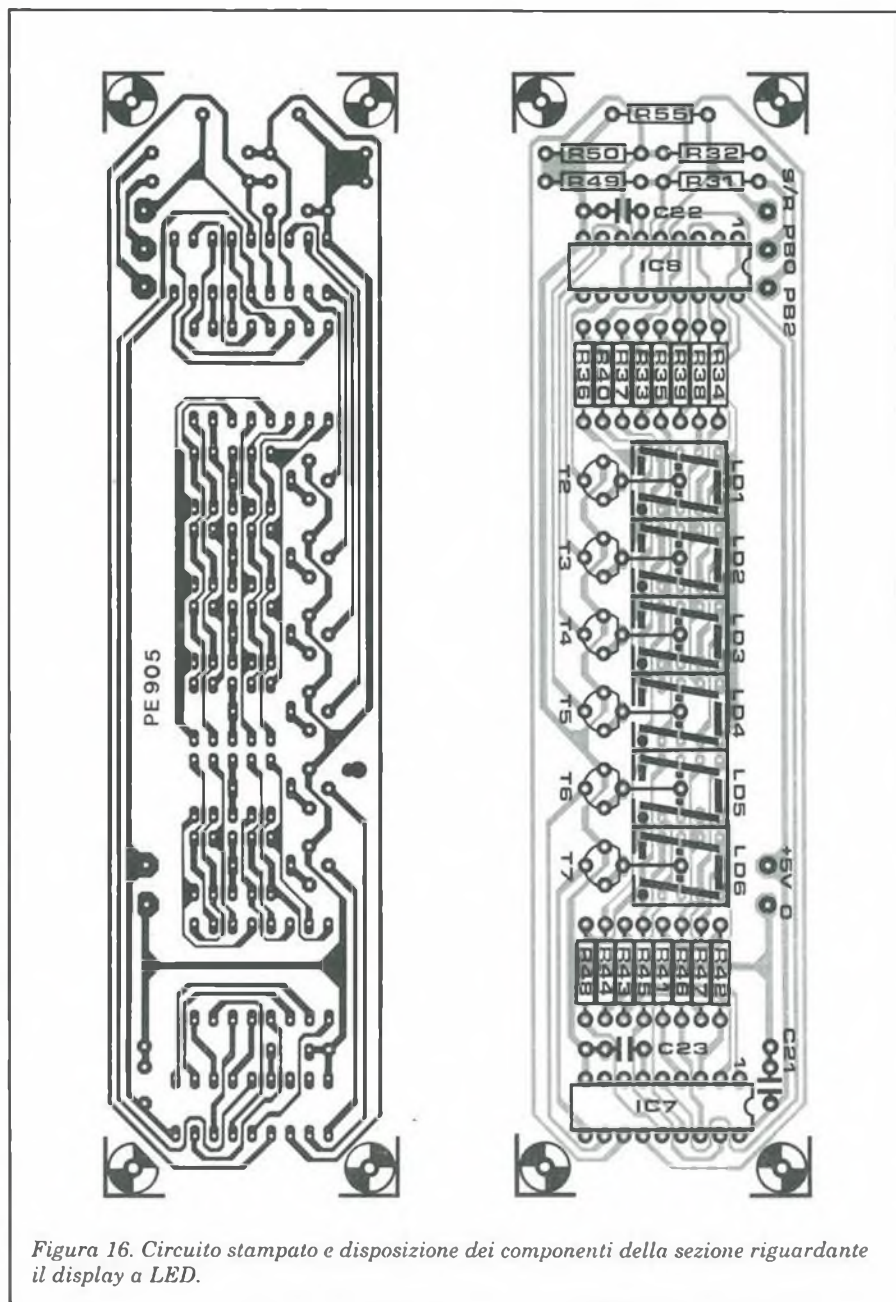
Circuito stampato e disposizione dei componenti della sezione riguardante il display a LED.
